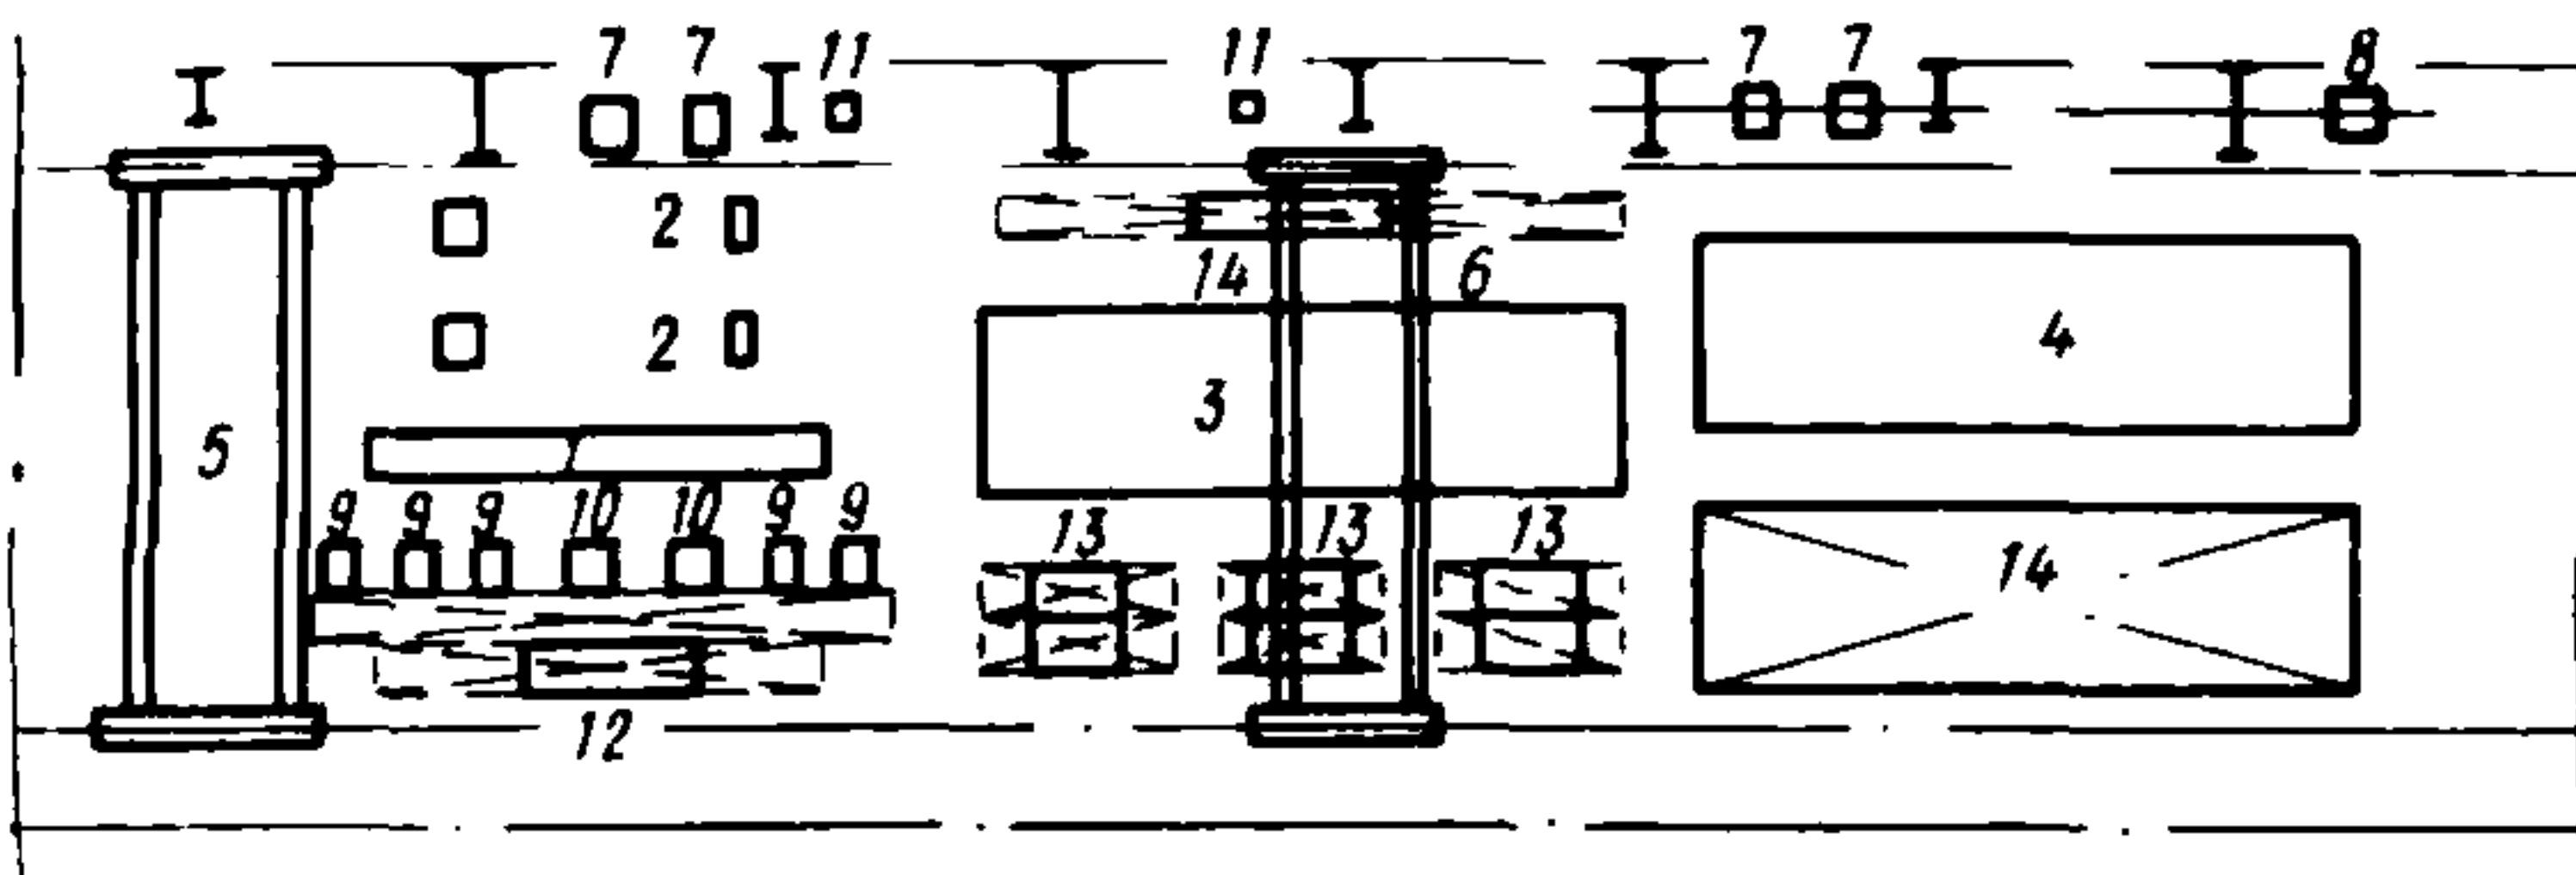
Планировка участка сборки и сварки ферм из труб
